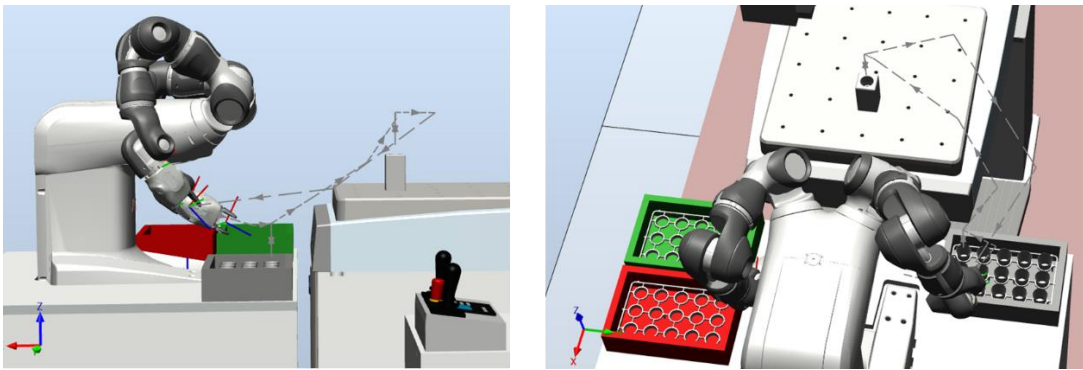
Zobrazení nástroje robota ve všech vytvořených targetech
